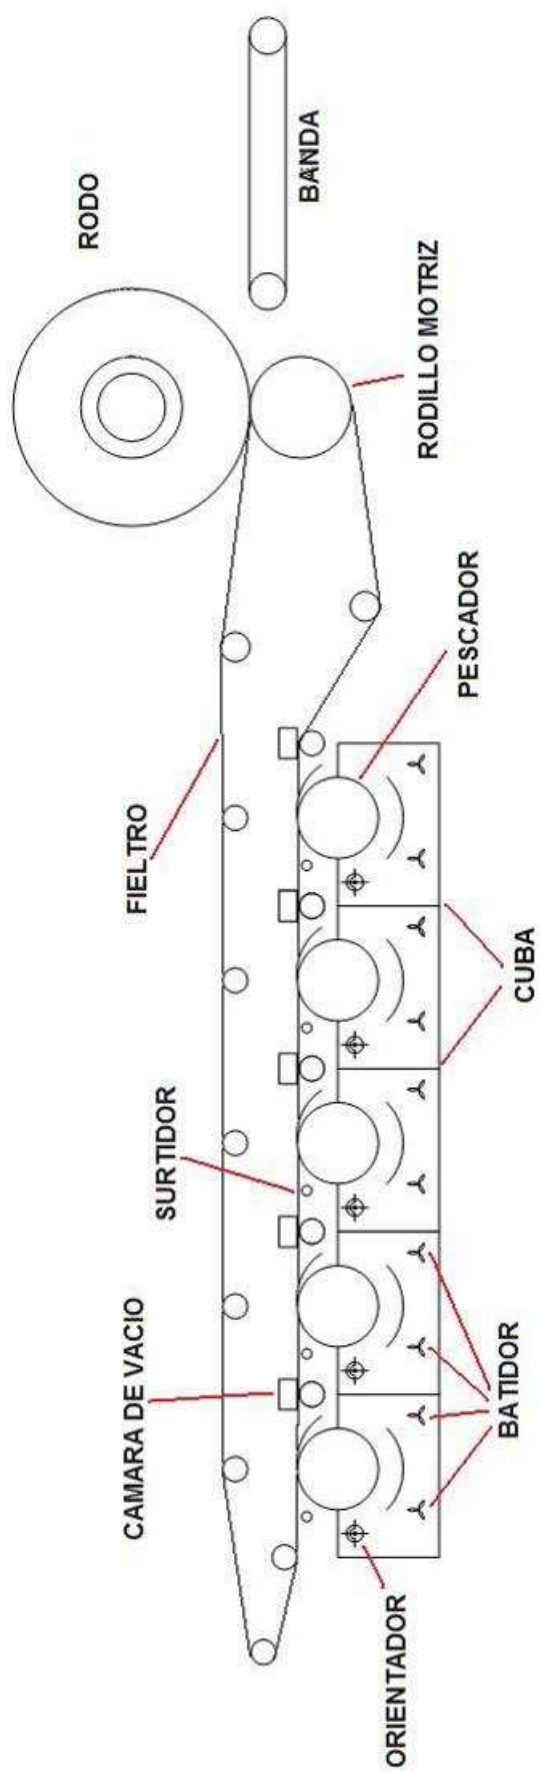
Esquema maquina Hatscheck de laminación de cemento en donde se detallan sus partes principales
